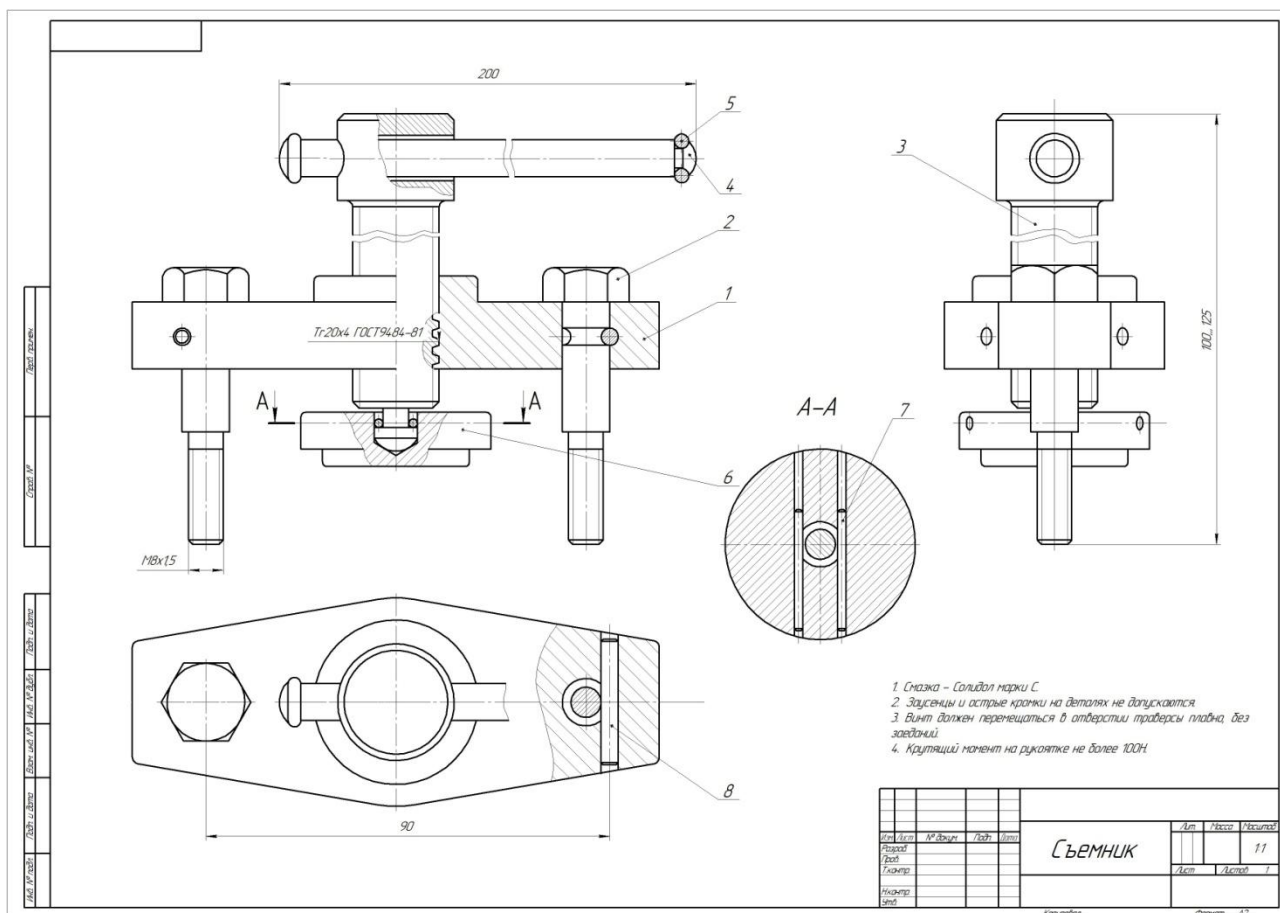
Исходный чертеж приспособления «Съемник»: 1 – траверса; 2 – болт (2 шт.); 3 – винт; 4 – ручка; 5 – кольцо; 6 – пята; 7 – штифт (2 шт); 8 – штифт (2 шт).
